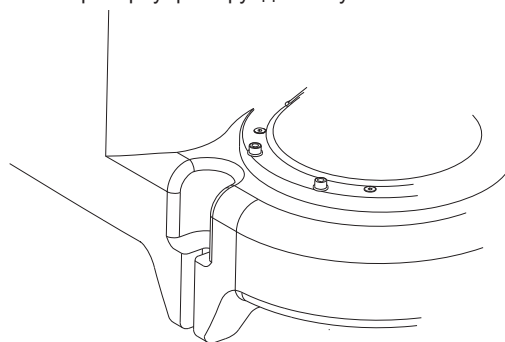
Точка крепления для монтажа резервуара на фундаменте
